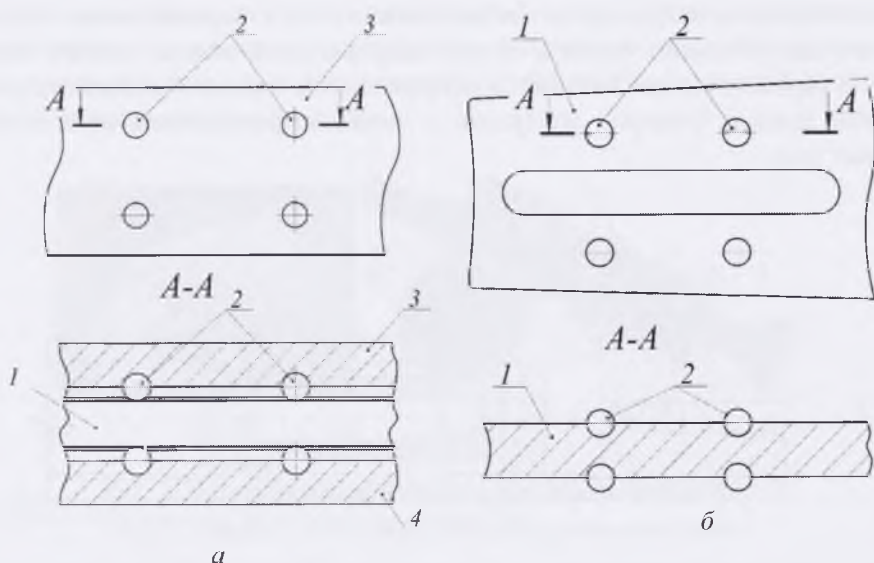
Конструкции подвижной пильной шины с вставленными направляющими шариками: *а* – в корпусе и крышке; *б* – в пильной шине (*1* – шина; *2* – направляющие шарики; *3* – корпус; *4* – крышка)
